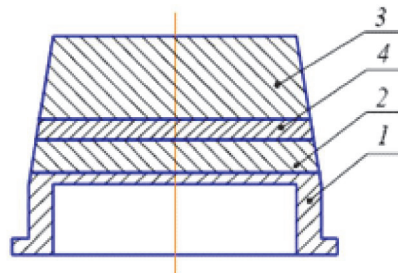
Конструкция четырехслойного СВС-прессованного катода
